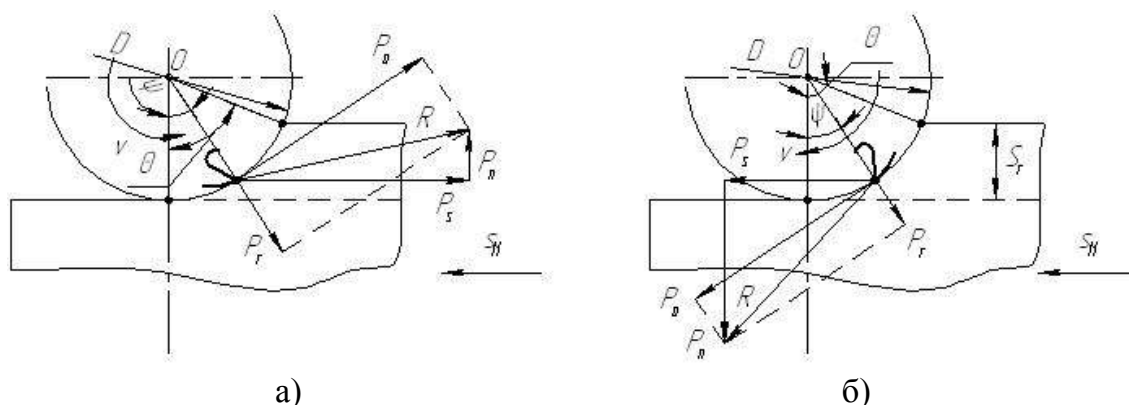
Схема сил, действующих при работе прямого зуба сферической фрезы (а - встречное фрезерование, б – попутное фрезерование) (упрощенно)
